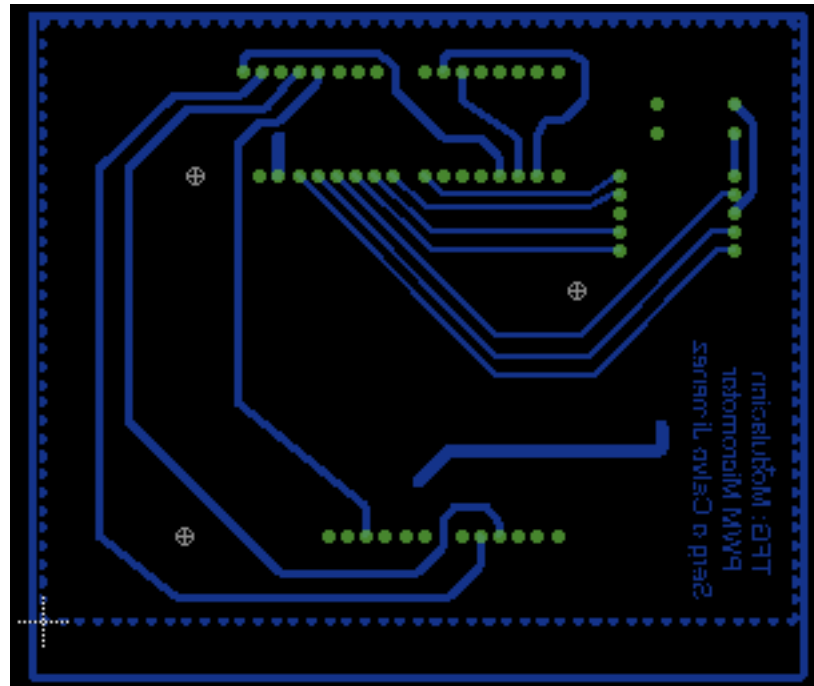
Rutas y PADs del circuito impreso PCB parte 2
